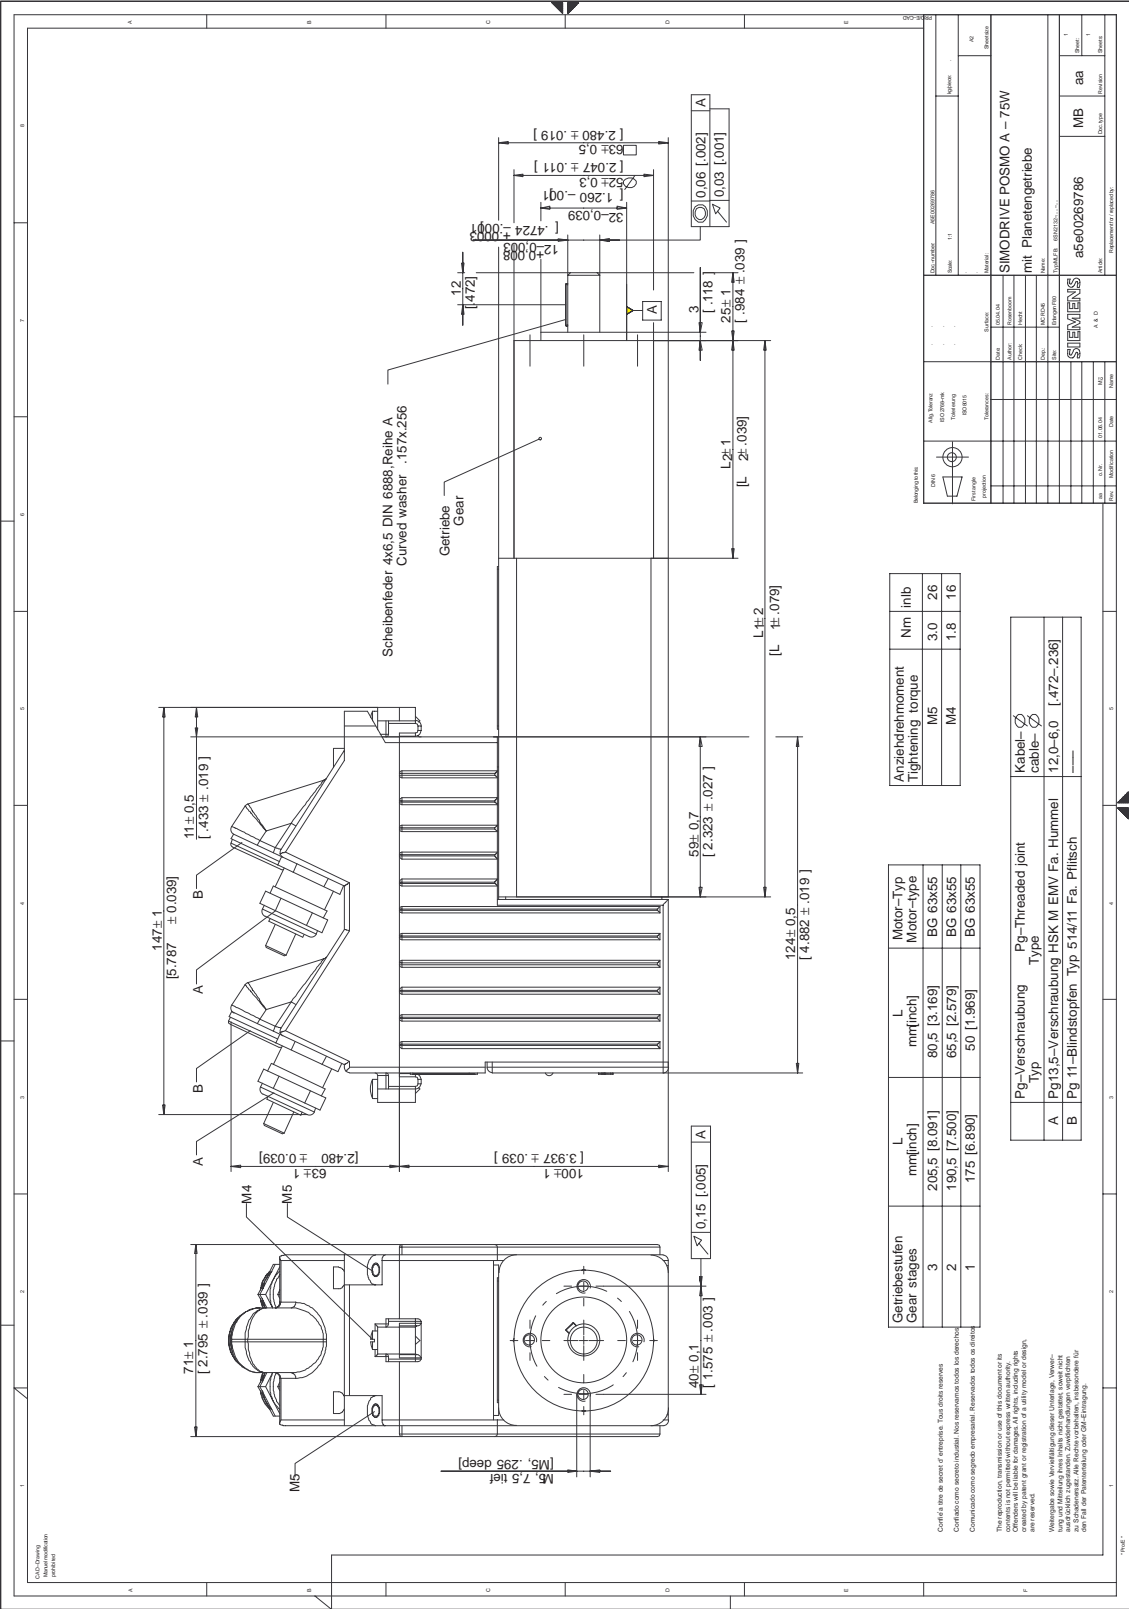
Maßblatt: SIMODRIVE POSMO A – 75 W mit Planetengetriebe
